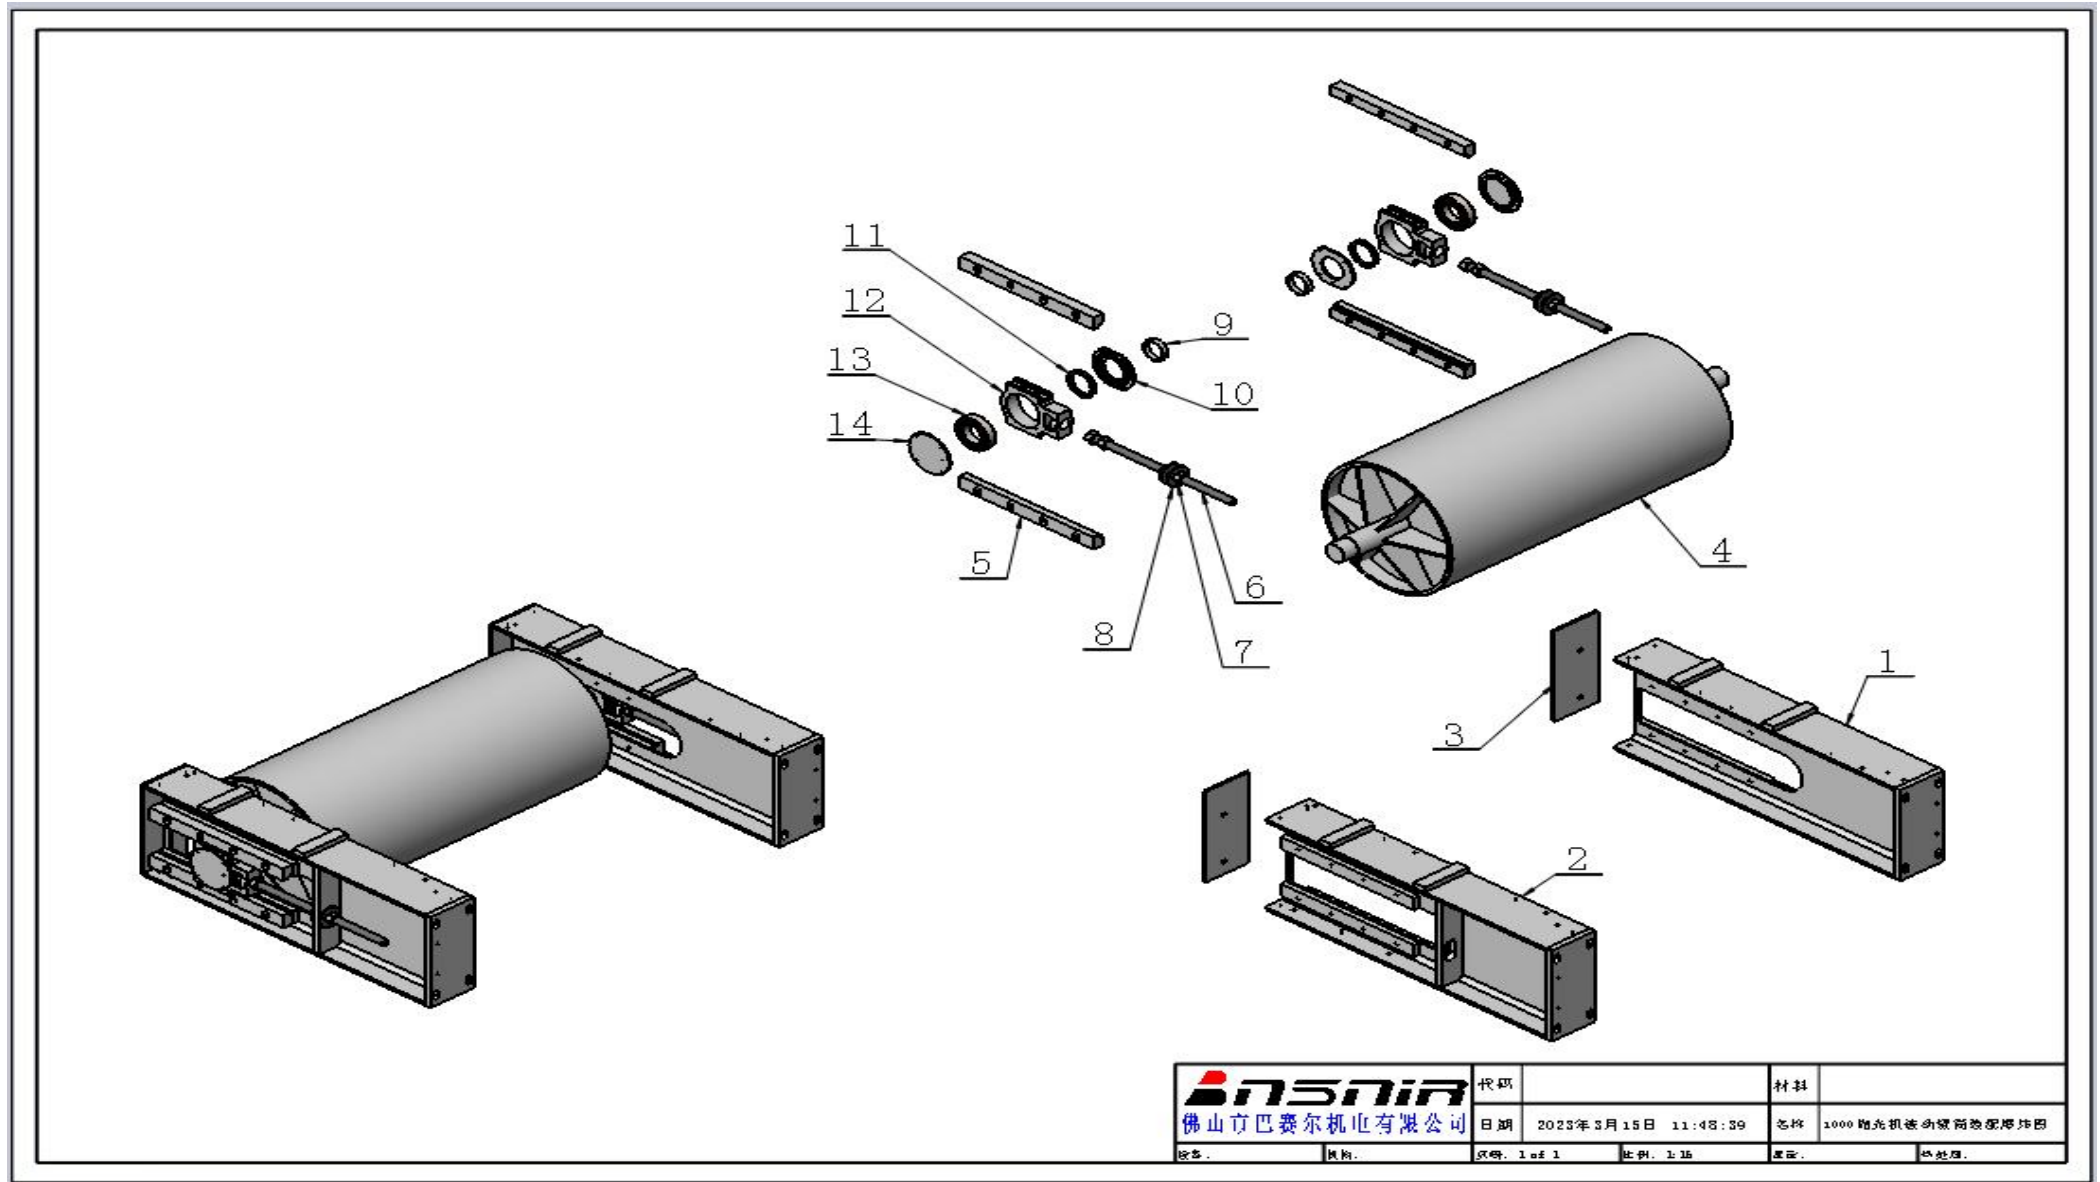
8 机架部分——被动辊筒组件装配图 picture2-8 Rack Part -- Assembly of passive roller assembly
